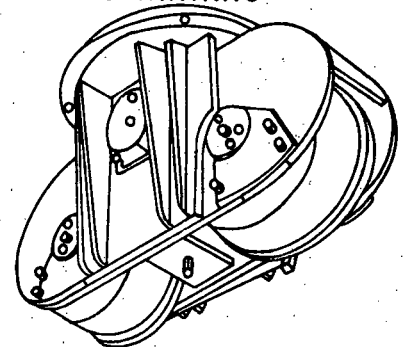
e FIG.2 MOSTRAM O ARRANJO DO SUPORTE DA FLANGE SUPERIOR PARA CARRINHO E RODA
